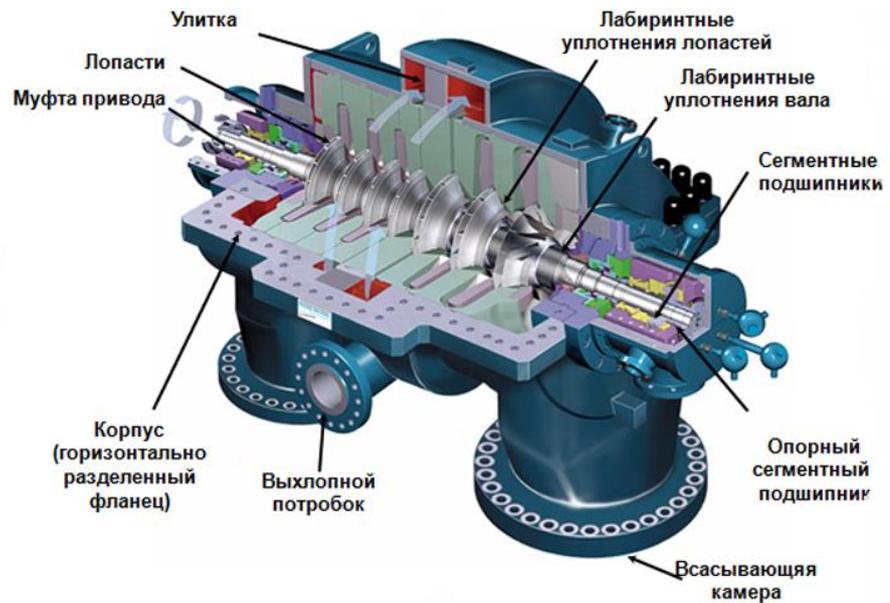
Схема устройства многоступенчатого центробежного компрессора:
